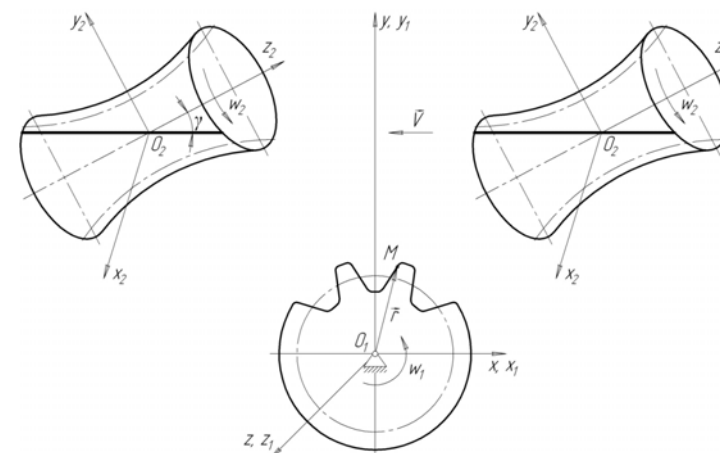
Схема изготовления винтовых зубчатых колёс
